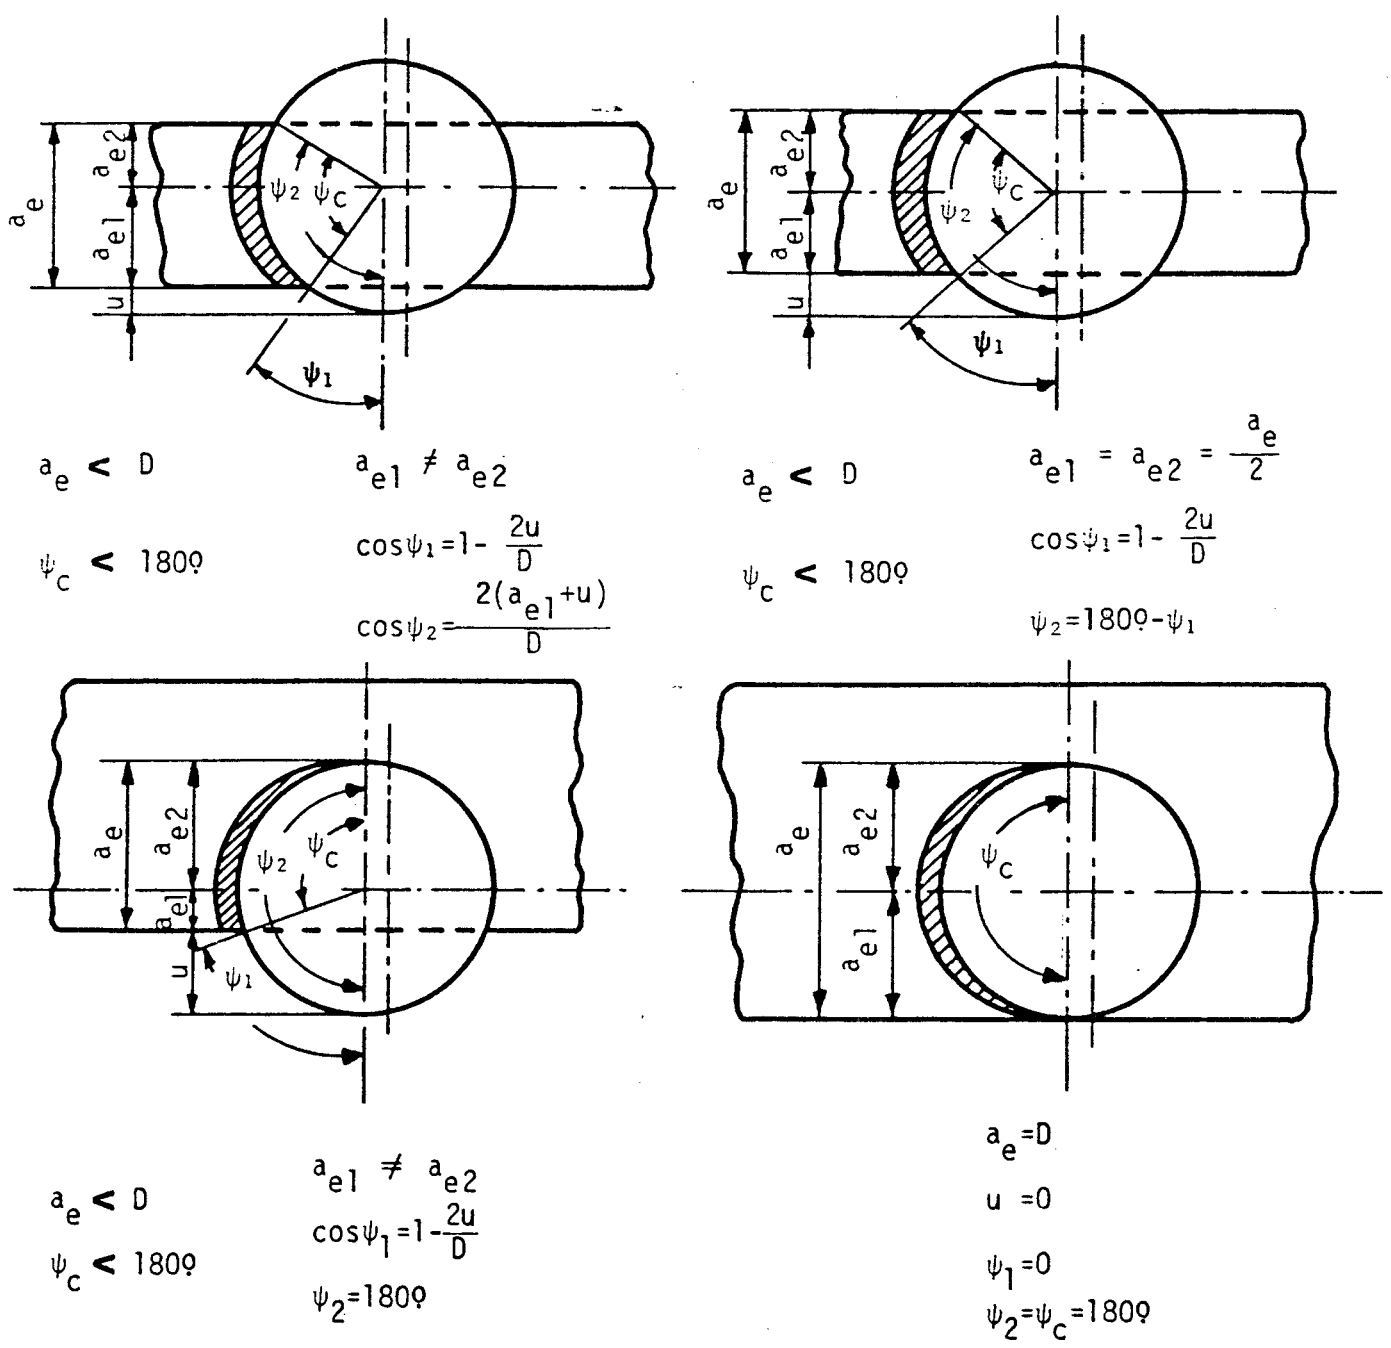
Fresamento frontal: relações de contato peça - ferramenta.
